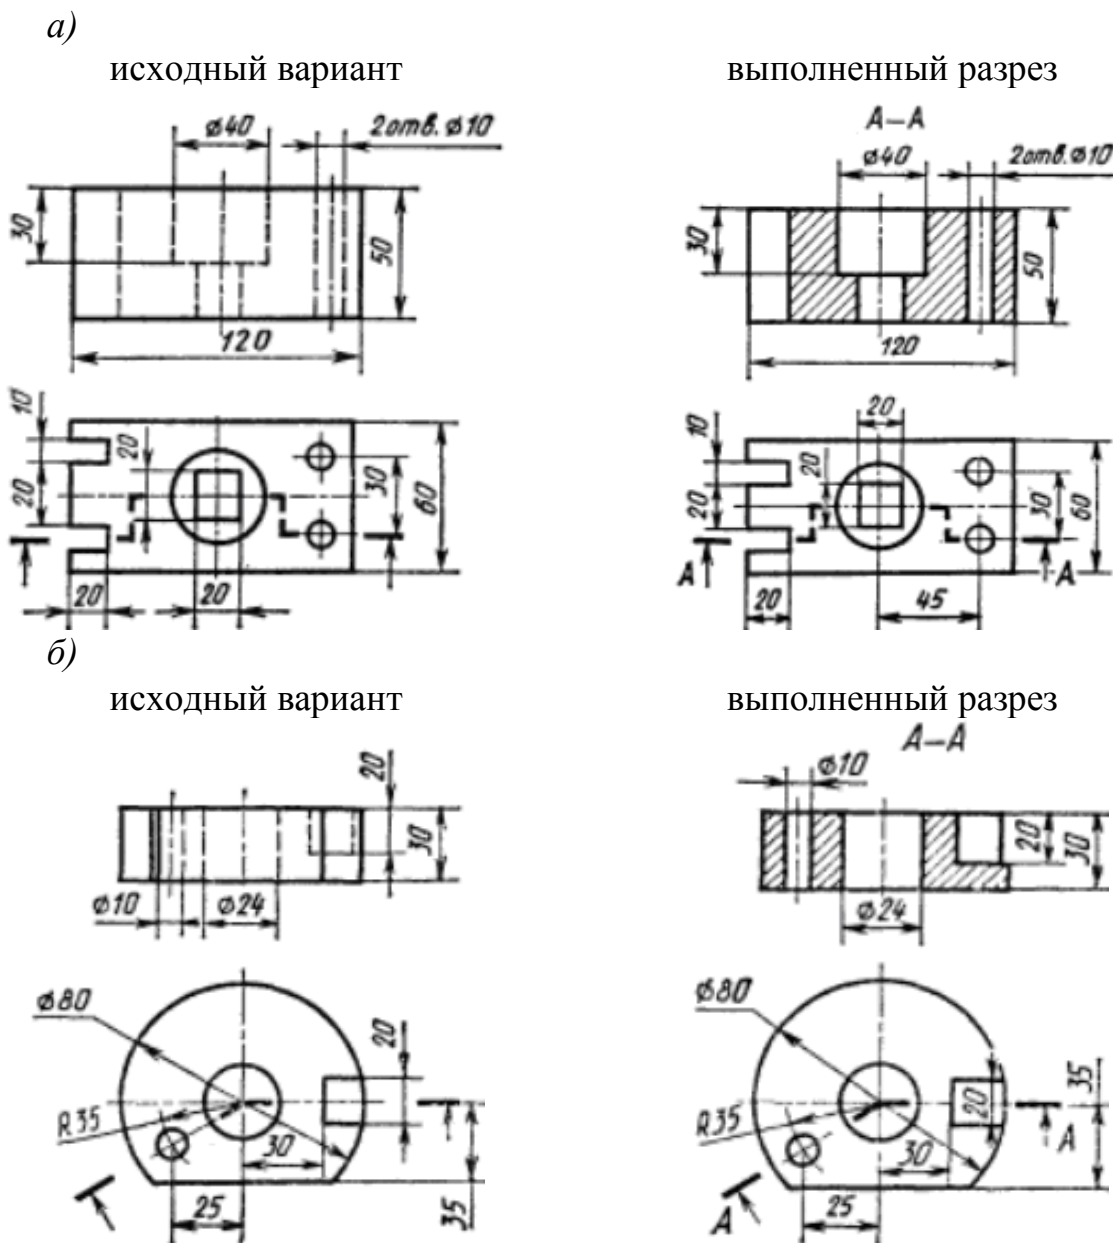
Образец графической работы «Разрезы»: а – ступенчатый разрез, б – ломаный разрез
